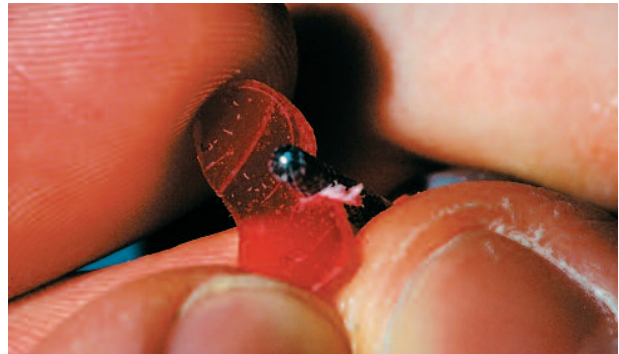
Das Herausschleifen des Rohlings mit einer Fräse.
